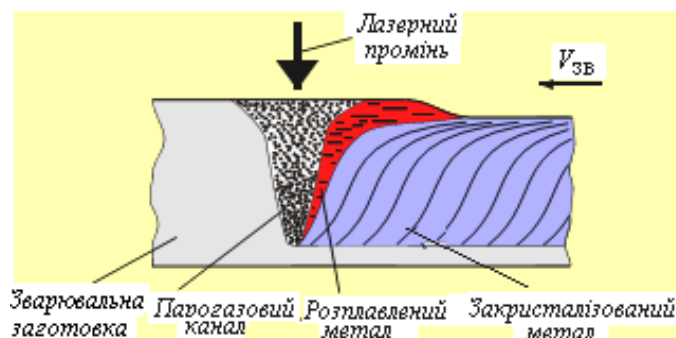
Схема формування зварного шва при лазерному зварюванні з глибоким проплавленням
